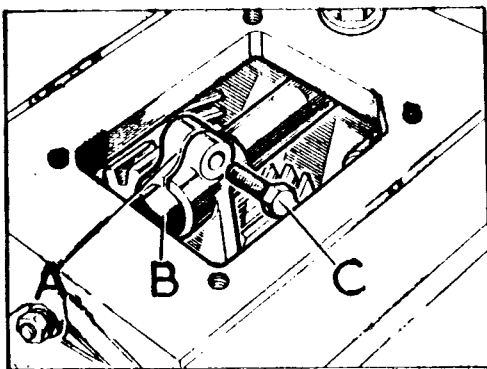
Conjunto de la horquilla selectora de la caja reductora
